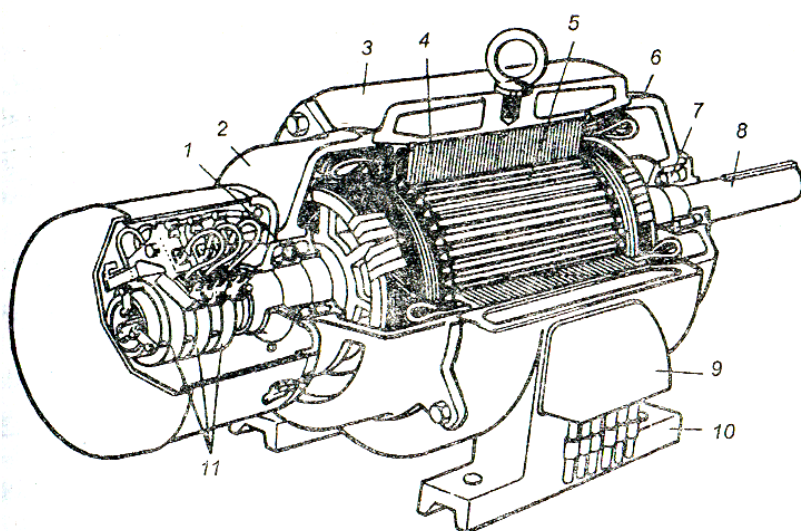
Устройство асинхронной машины с фазным ротором: 1, 7 – подшипники; 2, 6 – щиты подшипниковые; 3 – корпус; 4 – статор; 5 – ротор; 8 – вал; 9 – коробка выводов; 10 – лапы; 11 – фазные кольца
